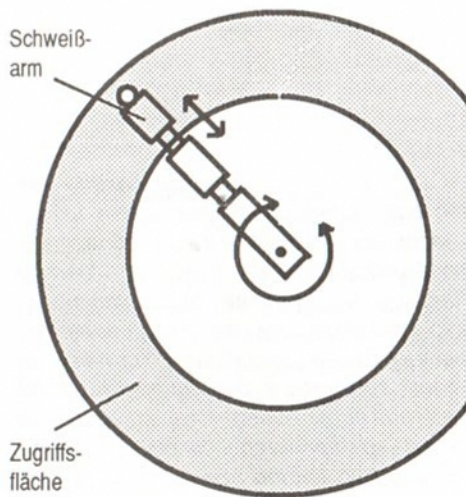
Zugriffsfläche des Schweißroboters.
